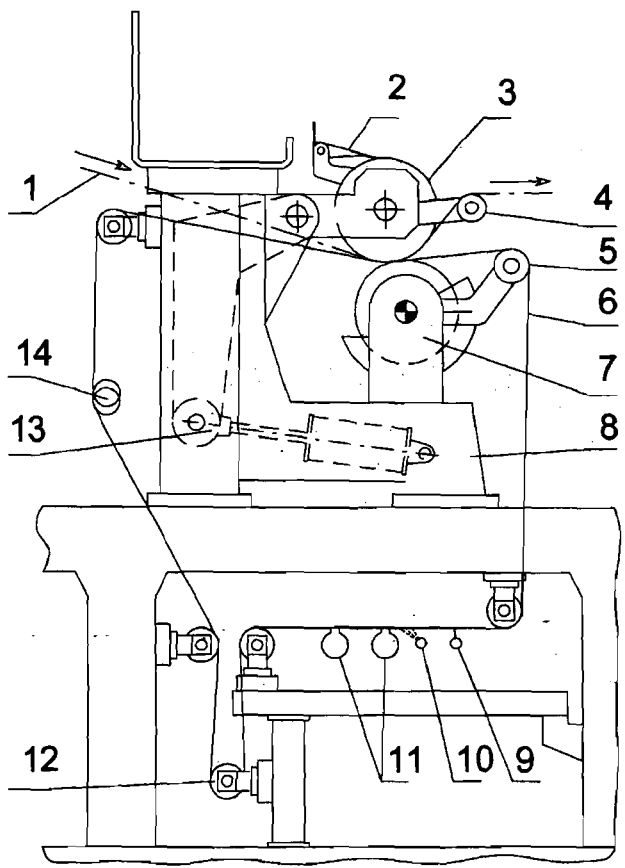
Обычный двухвальный пресс: 1 – бумажное полотно; 2 – шабер; 3 – верхний вал (гранитный); 4 – бумаговедущий валик; 5 – сукноведущий валик; 6 – прессовое сукно; 7 – нижний вал (обрезиненный); 8 – станина пресса; 9 – спрыск высокого давления; 10 – спрыск низкого давления; 11 – сукномойки; 12 – сукнонатяжной валик; 13 – механизм прижима валов; 14 – сукноправильный валик
